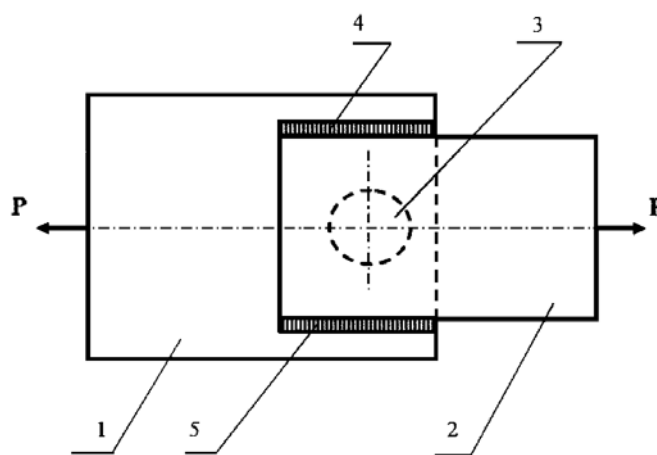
Налесточное сварное соединение с продольными угловыми швами дополненное сварной точкой:
